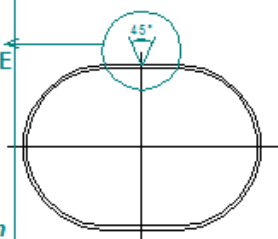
DETAIL assemblage surbau/pièce rep.2 (Vue de dessus)
